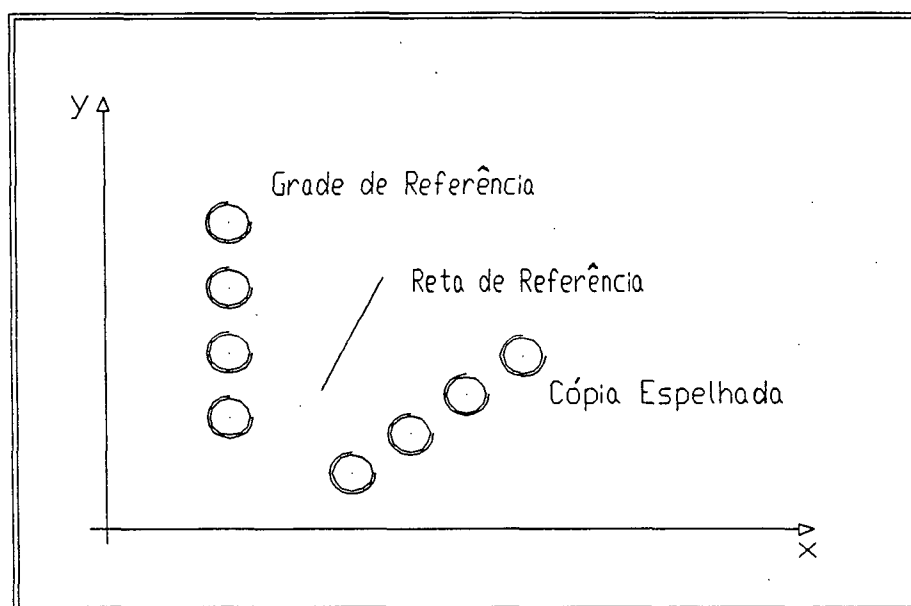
Espelhamento aplicado sobre disposição de furos em linha.
